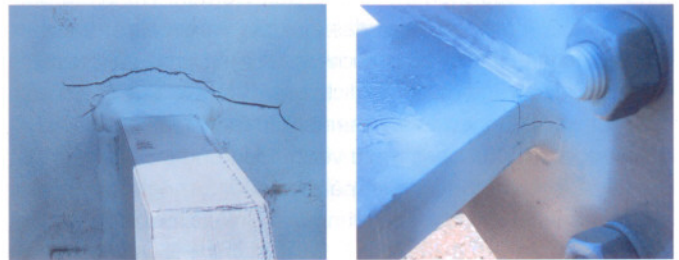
Mit blosssem Auge nicht erkennbar – Verzinkungsrisse an einer eingesteckten Lasche mit Dickensprung vom Blech zum Walzprofil nach der MT-Prüfung
